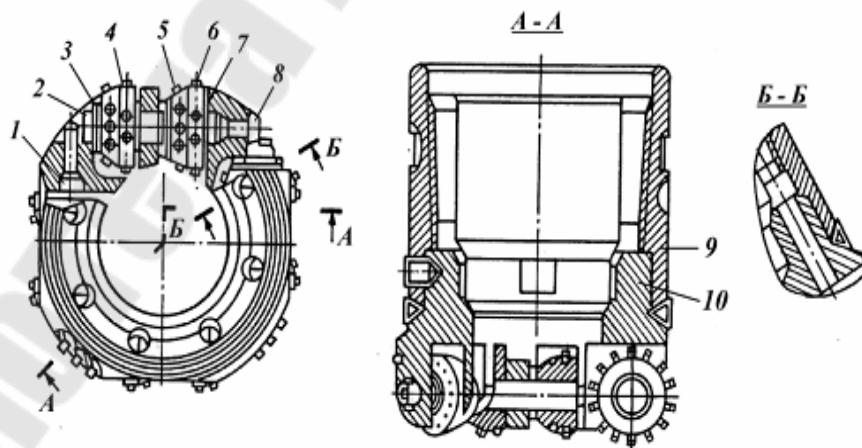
Восьмишарошечная бурильная головка режущего действия, с шарошками, оснащенными твердосплавным, карбидвольфрамовым вооружением (зубками): 1 – запорный хвостовик; корпус; 2 – опорная ось; 3 – шайба; 4 – скважинообразующая шарошка; 5 – калибрующие твердосплавные подрезные зубки с плоской рабочей частью; 6 – основные режущие твердосплавные клиновидные зубки, формирующие керн (шарошкой 7) и
